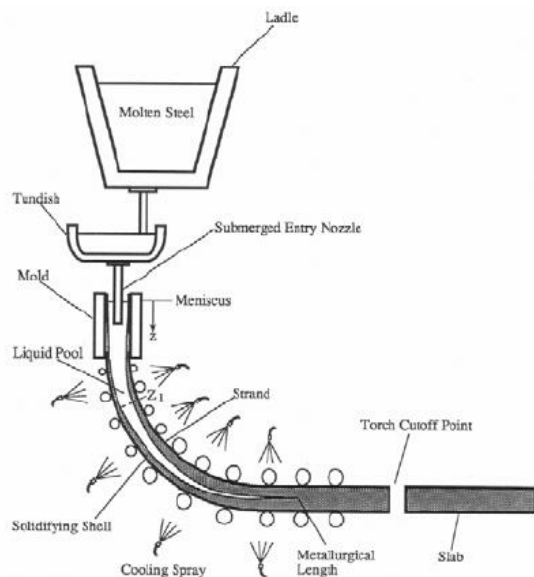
Схематичне зображення машини безперервного лиття заготовок
